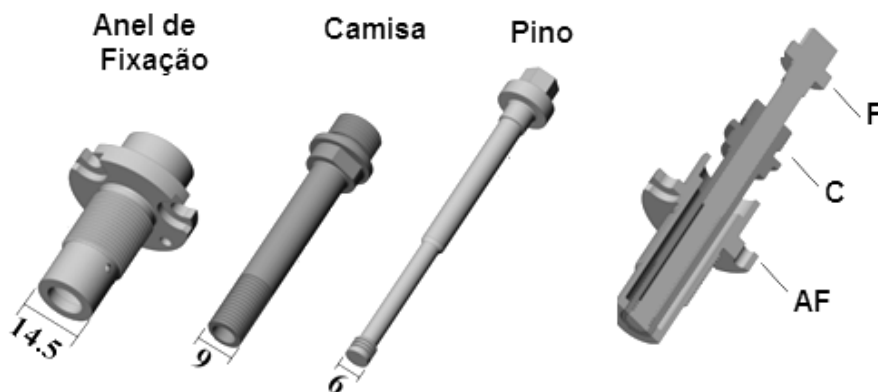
Ilustração esquemática da ferramenta utilizada em FSpW e seus componentes (dimensões em mm).
